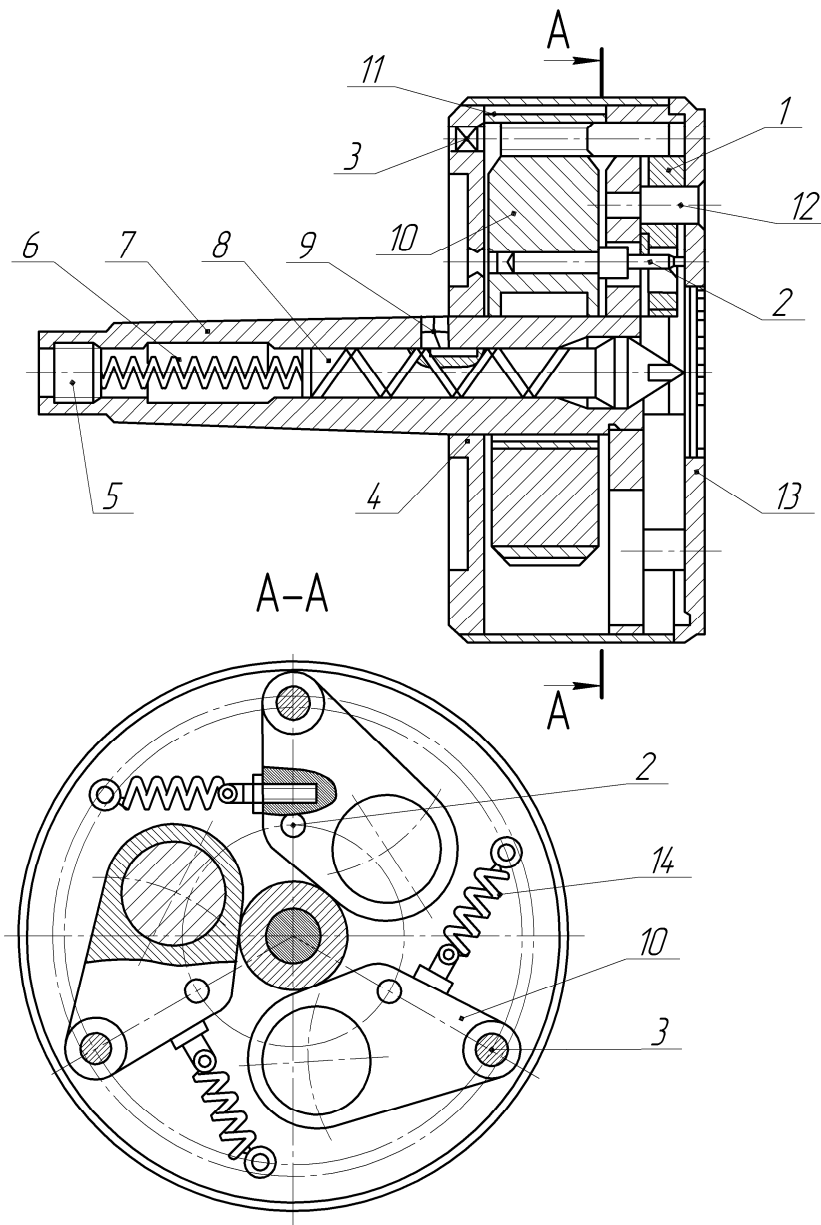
Будова трикулачкового повідкового патрона: 1 – кулачок; 2 – палець; 3, 12 – осі; 4 – корпус патрона; 5 – нарізна пробка; 6 – пружина; 7 – конусна частина корпусу; 8 – плаваючий центр; 9 – гвинт; 10 – противага; 11 – кожух; 13 – кришка; 14 – пружина
